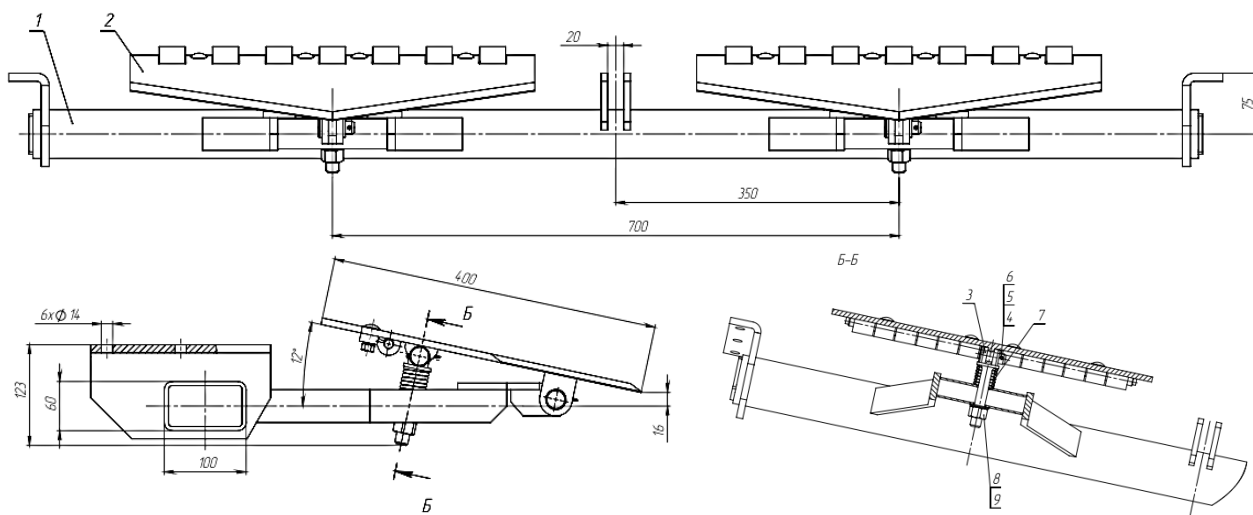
Разработанный подкапывающий рабочий орган для картофелеуборочной машины:
